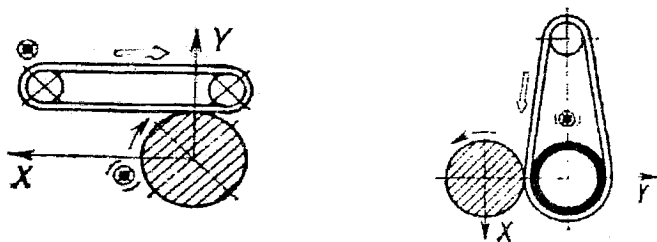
Полірування зовнішніх циліндричних поверхонь стрічками
